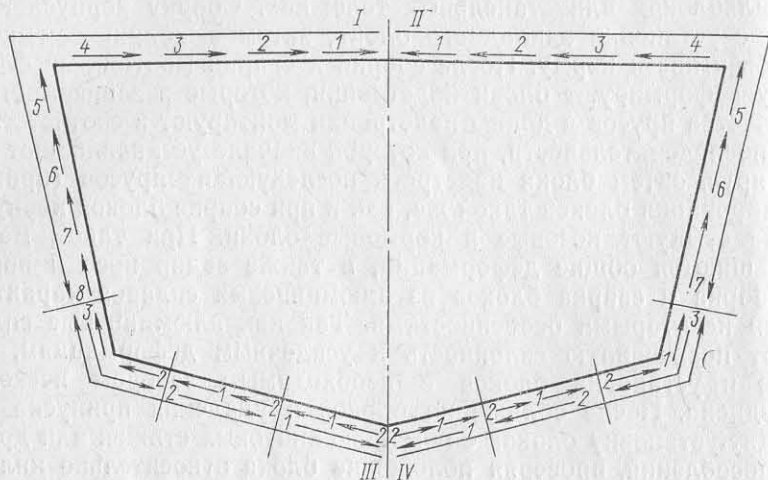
Схема сварки монтажных стыков корпуса.
